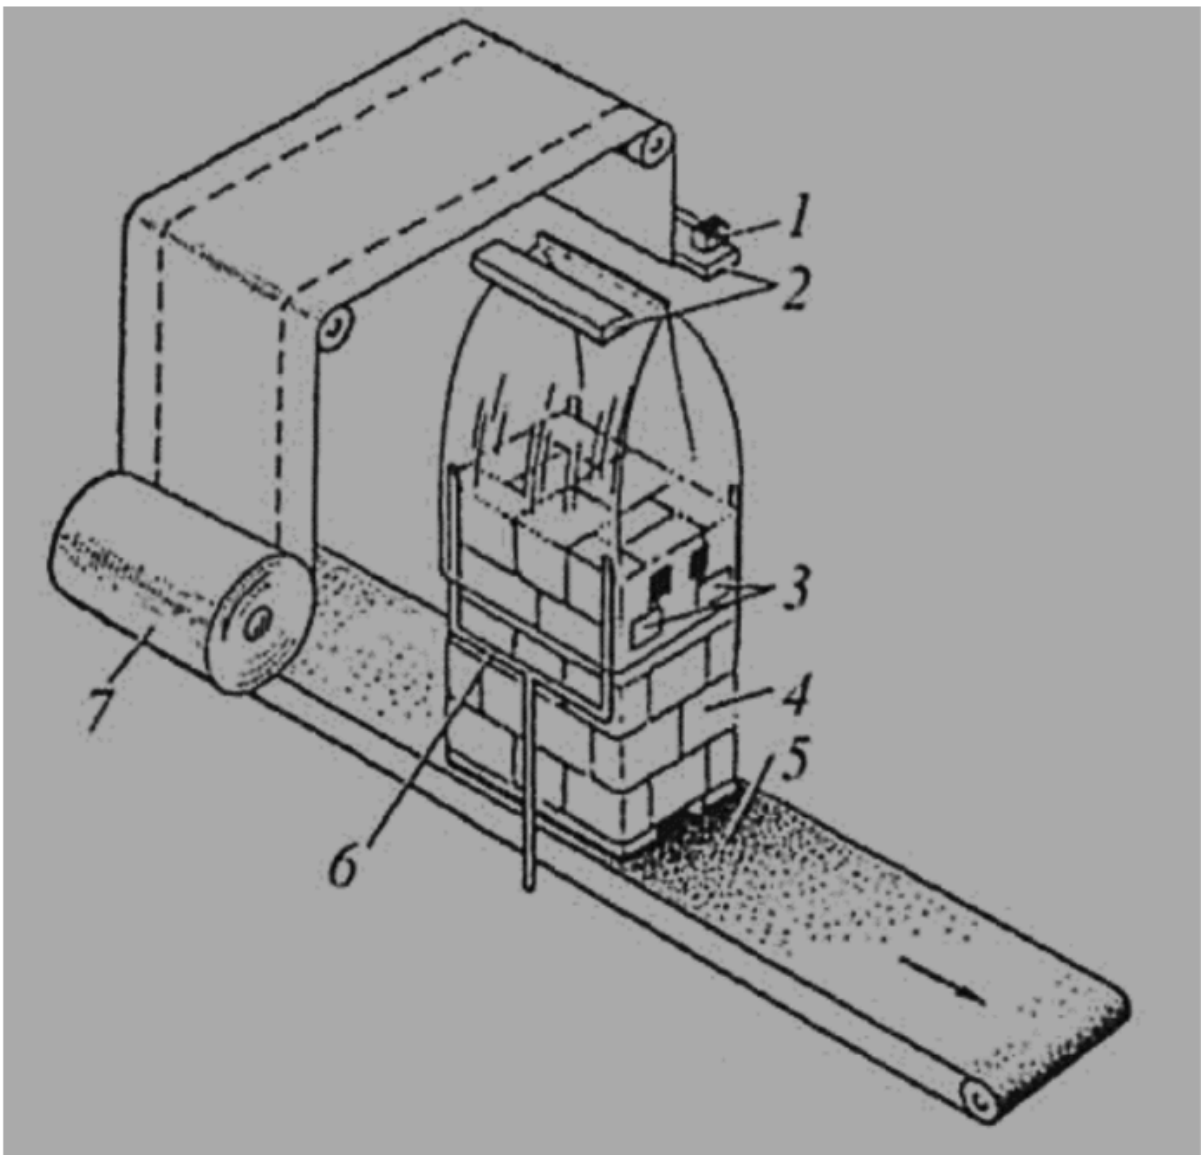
Технологічна схема машини закріплення транспортного пакету за допомогою термозбіжного чохла: 1 — різальний пристрій; 2 — зварювальні колодки; 3 — пневматичні захоплювачі; 4 — пакет вантажу на піддоні; 5 — конвеєрна стрічка; 6 — вила для розтягування плівкового чохла; 7— рулон плівки
